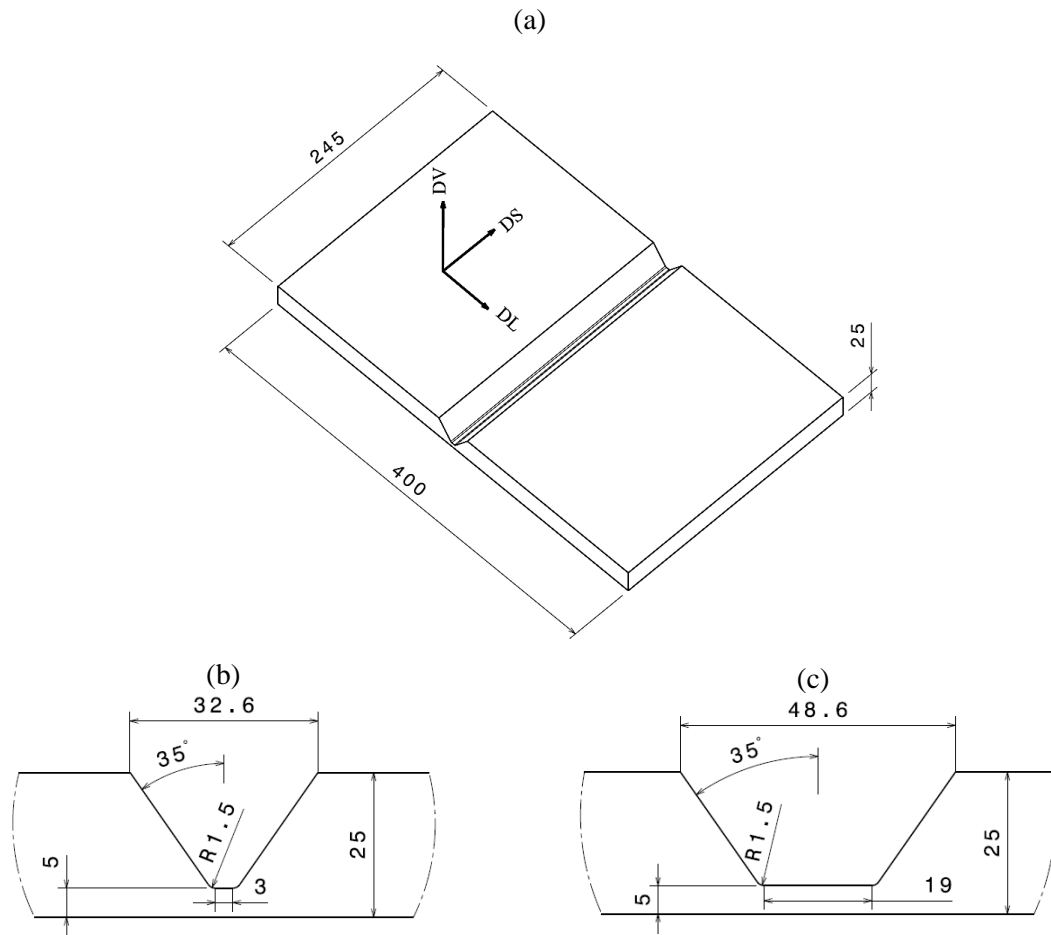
Définition des maquettes, dimensions de la plaque soudée et repère de travail (a), et dimensions du chanfrein, version 1 (Cv1) (b) et version 2 (Cv2) (c).
